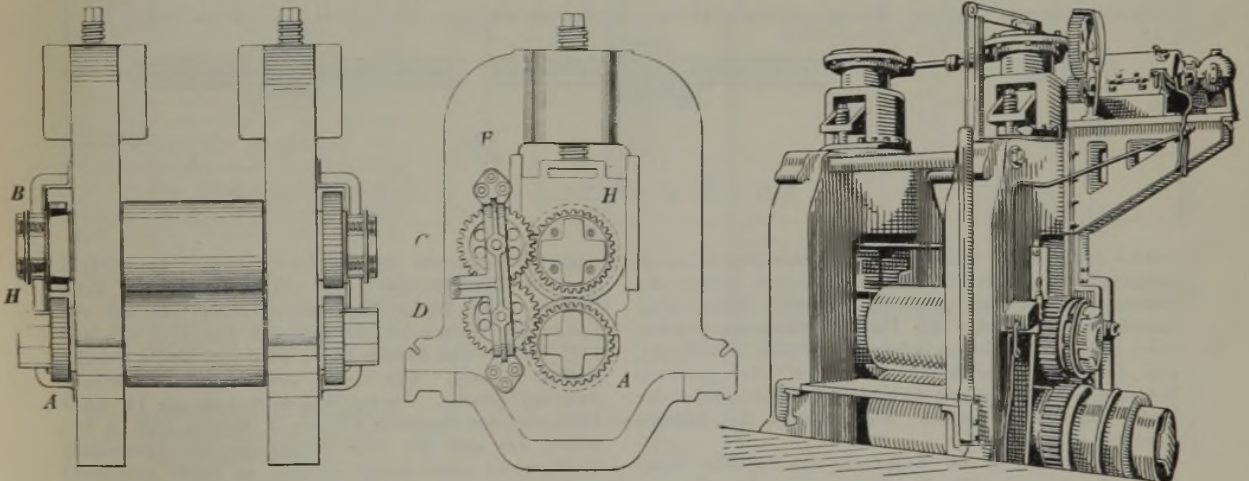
Walzenantrieb für Blechwalzgerüste Bauart Roemer.
